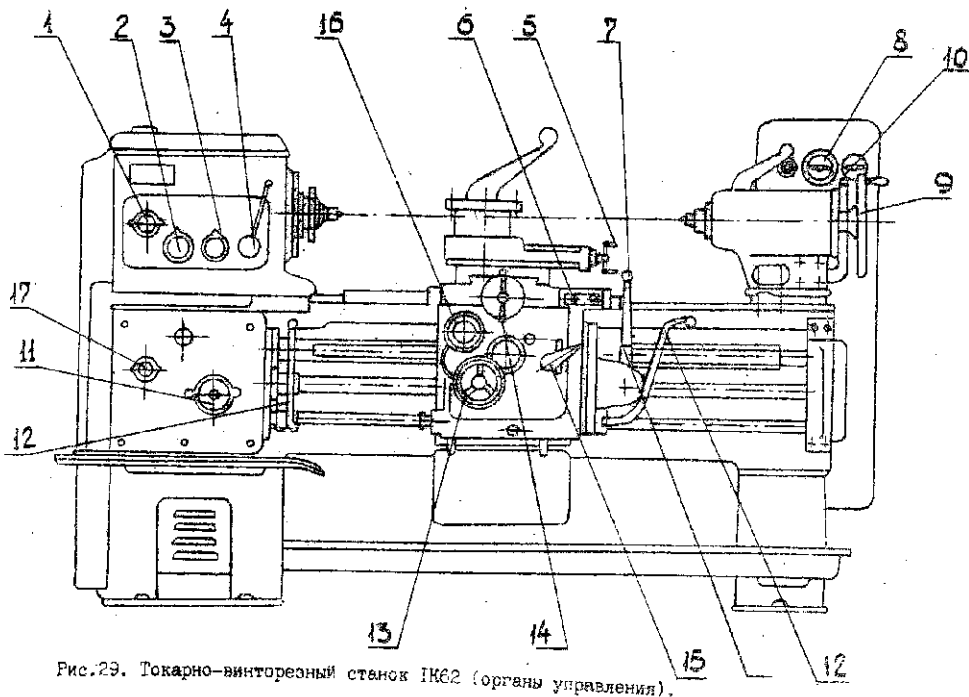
Токарно-винторезный станок 1К62 (органы управления).
